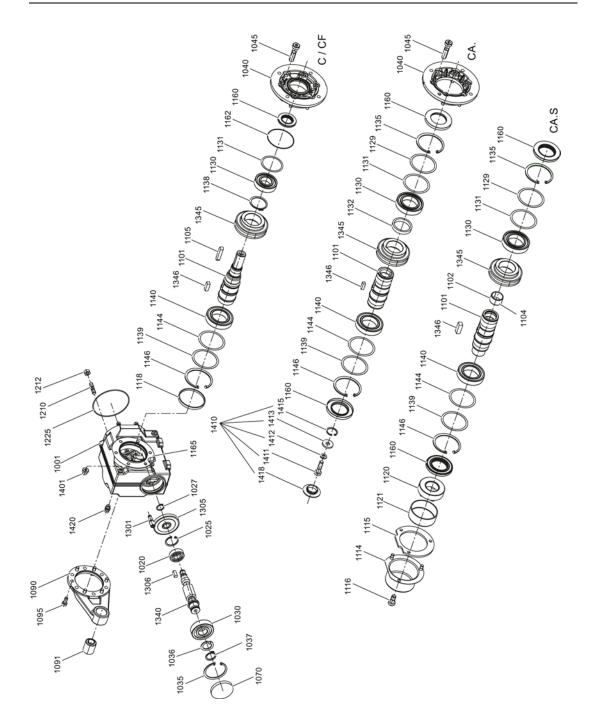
Reductor de ejes perpendiculares K, tamaños 39 - 149
